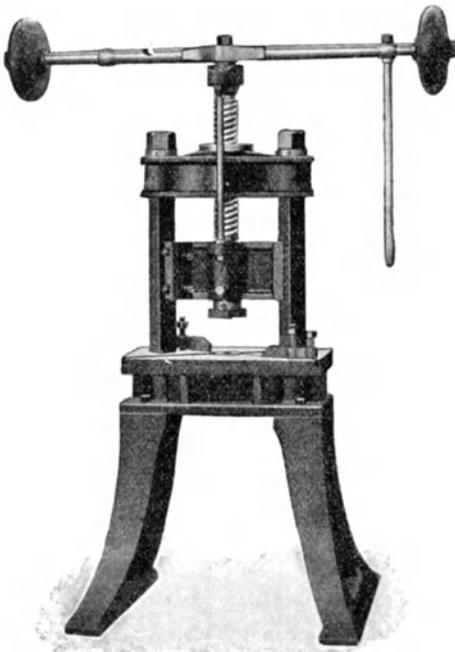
Spindelpresse zum Aufschweißen von Schnellstahl.
